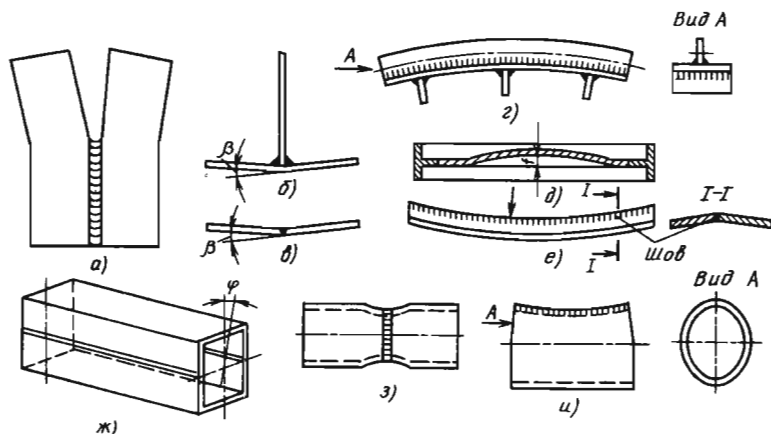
Виды сварочных деформаций и перемещений
